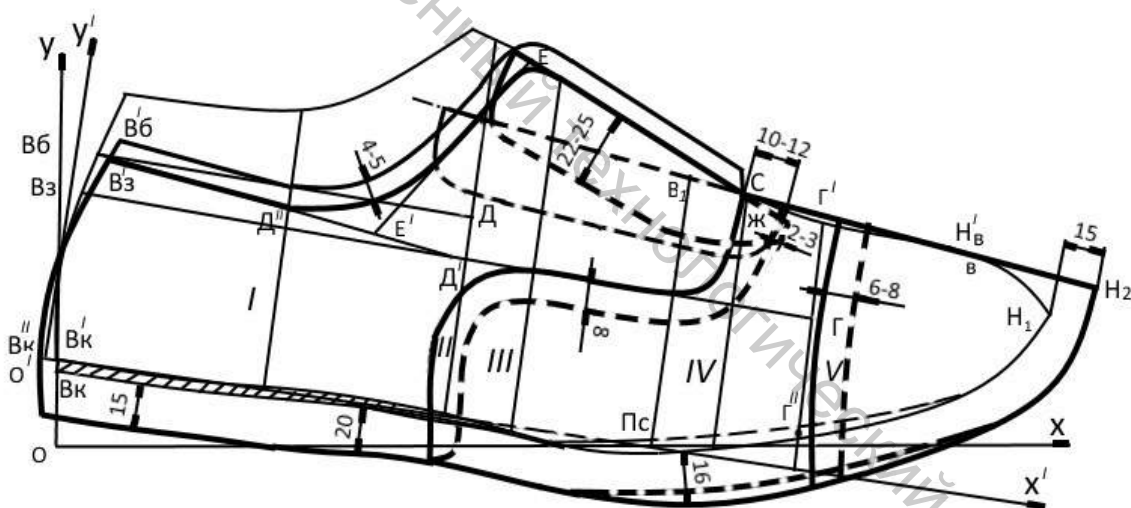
Построение верха полуботинка с настрочной союзкой
